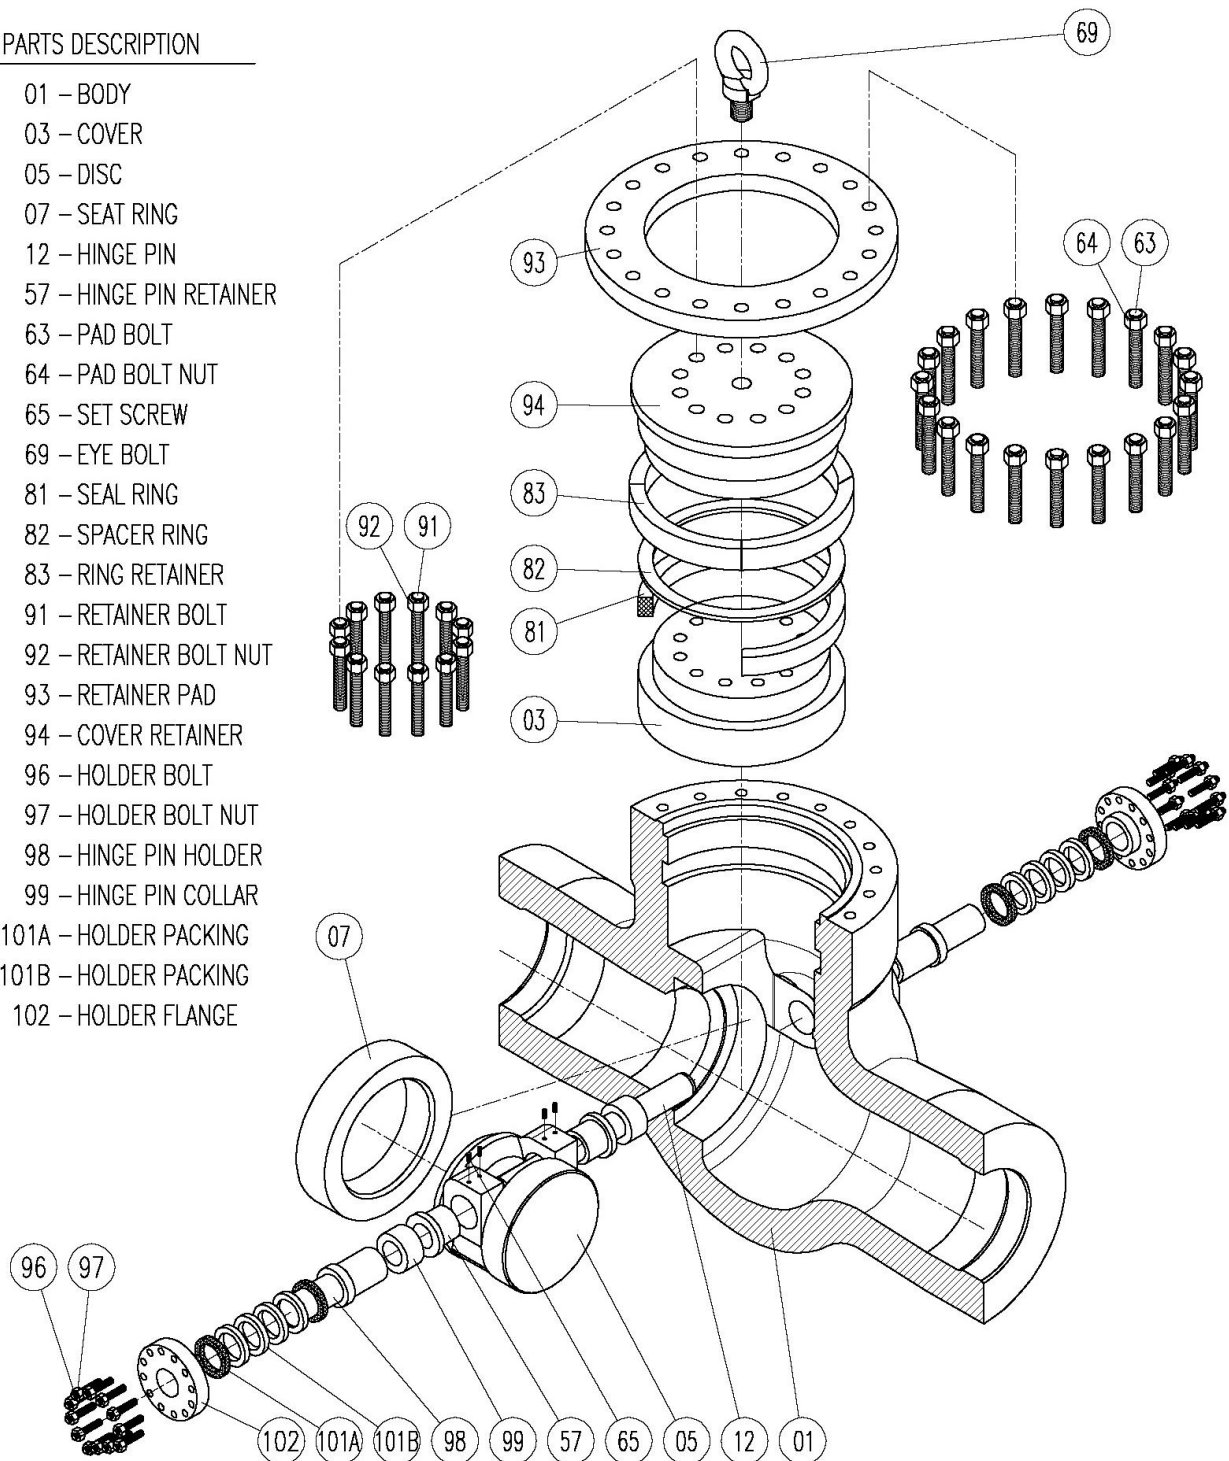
PRESSURE SEAL COVER TILTING CHECK 밸브 분해도
